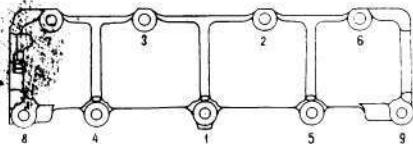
Порядок затягивания гаек крепления корпуса подшипников распределительного вала
